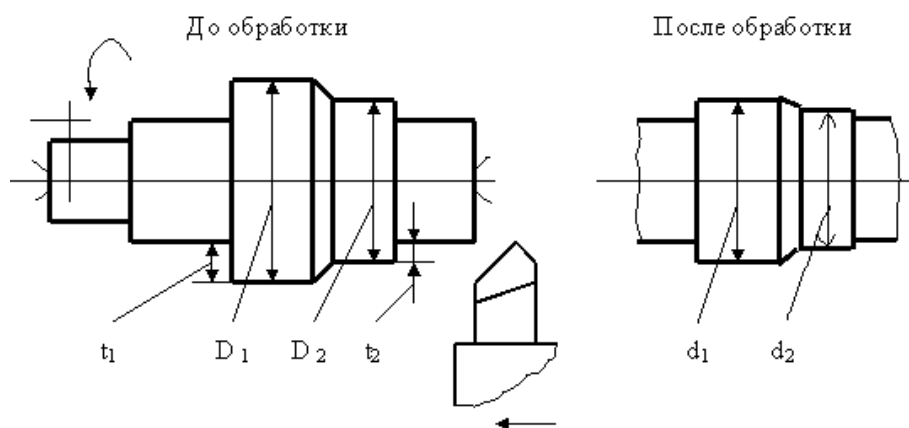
Схема испытания токарного станка для определения его динамической жесткости
